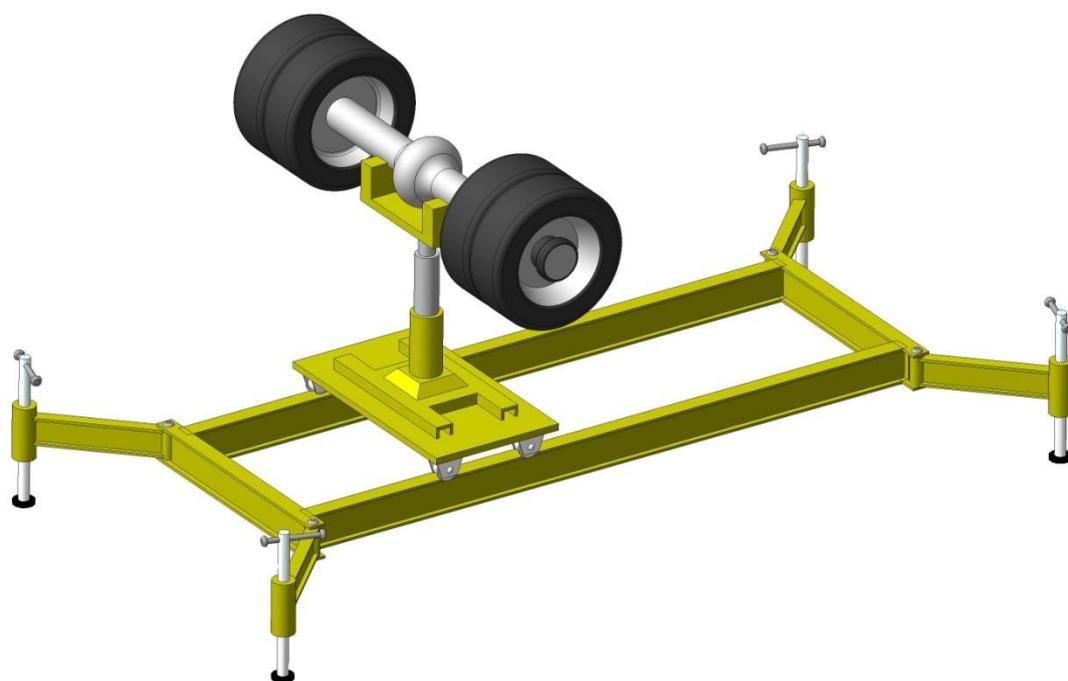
Общий вид устройства П248 для замены агрегатов автомобилей
